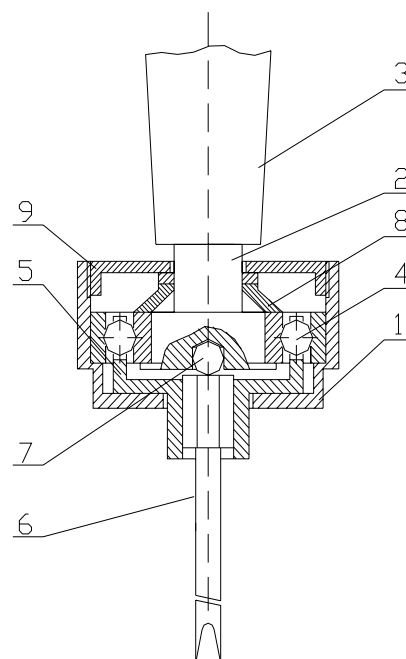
Конструктивная схема отвертки с устройством регулировки момента затяжки
